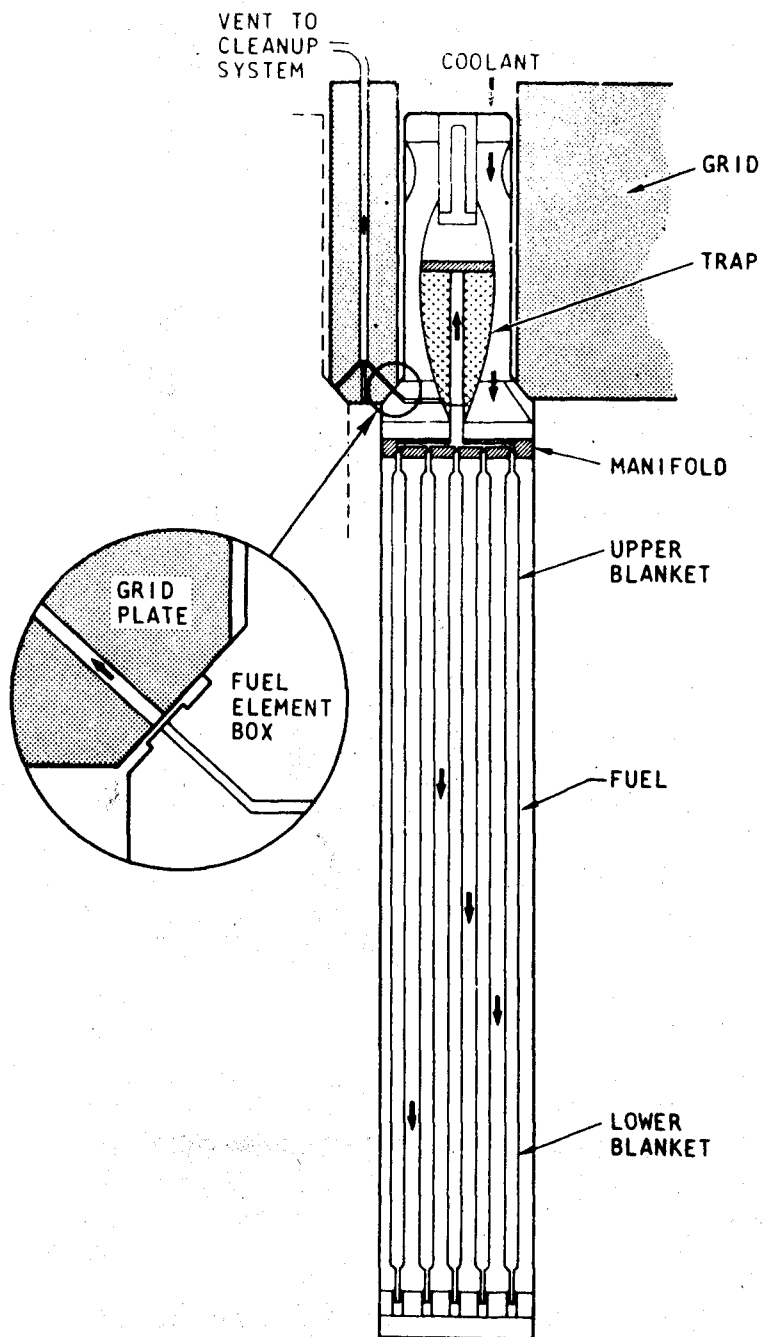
Conjunto de Elemento Combustível do GCFR
